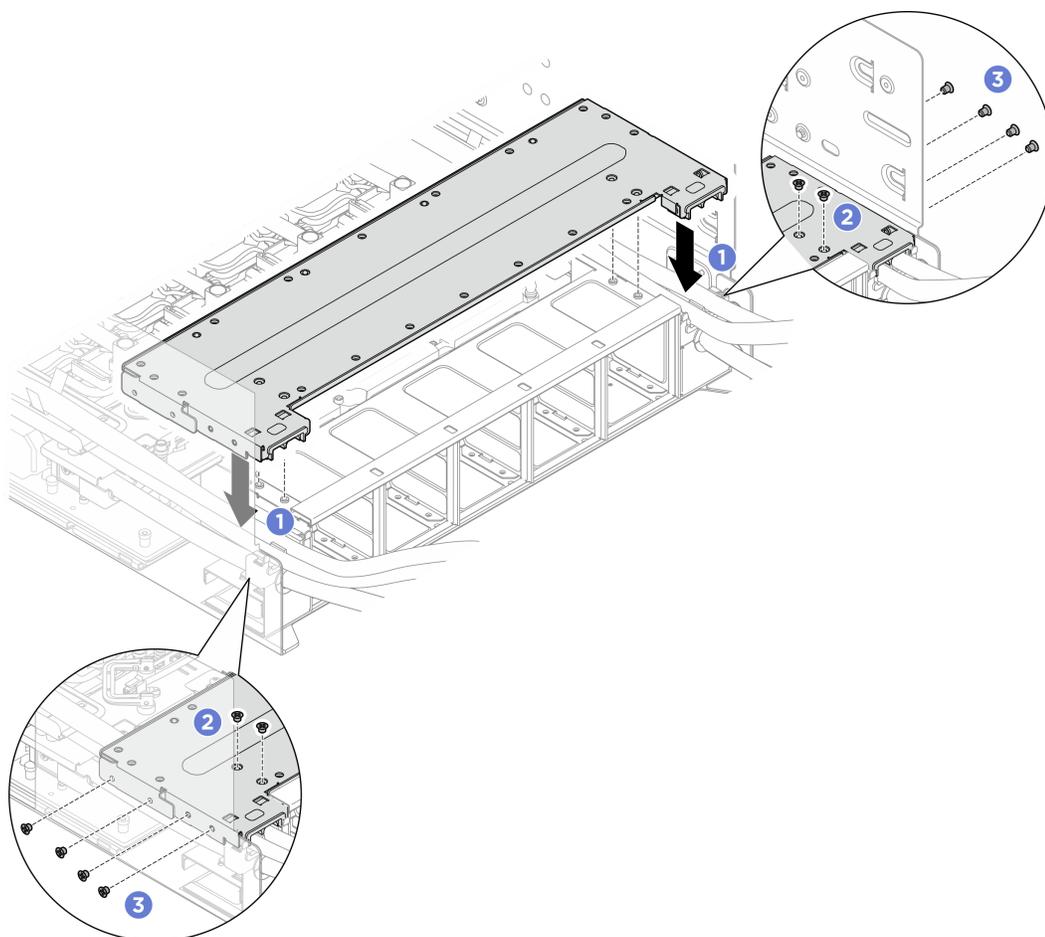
Instalando o suporte de apoio da gaiola do ventilador traseiro
